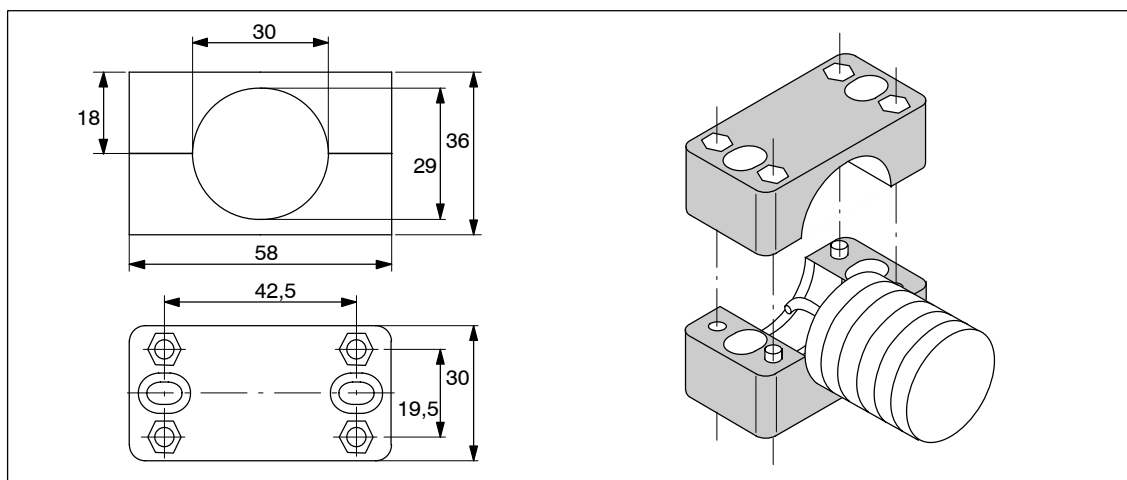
Montageskizze und Maßzeichnung SLG 40 mit Befestigungsschelle
